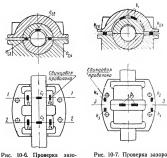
Проверка зазоров между валом и вкладышами подшипника.
